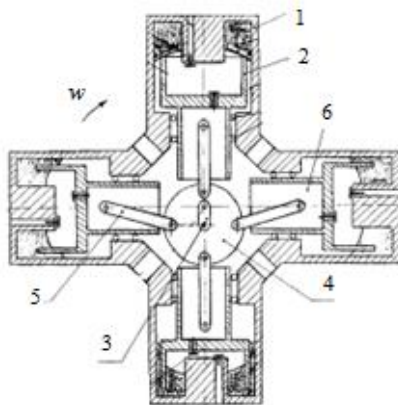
Конструктивна схема ротативного детандеру [5]: 1 – кільцевий блок циліндрів; 2 – поршень; 3 – нерухомий кривошип; 4 – диск; 5 – шатун; 6 – крейцкопф
